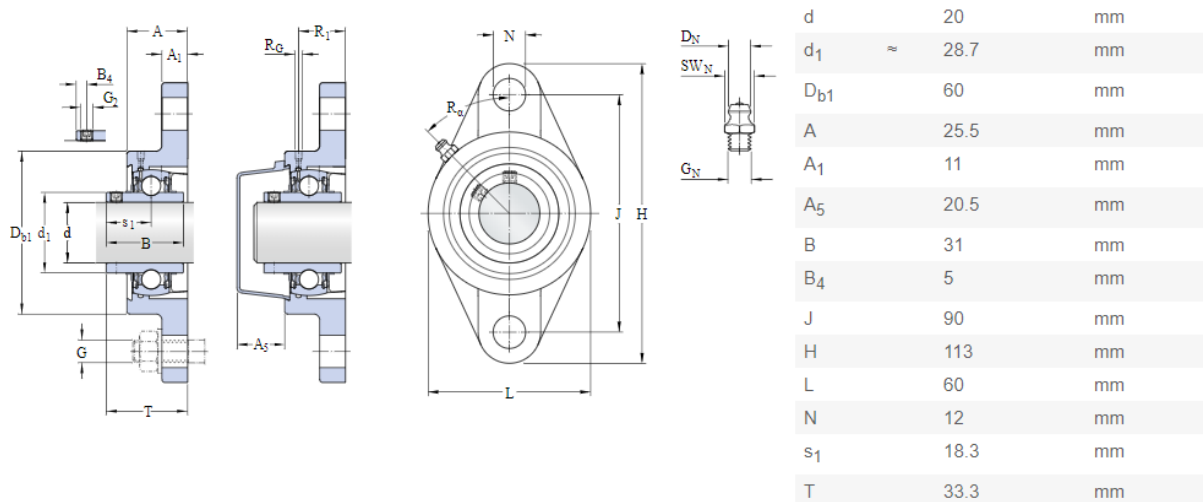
Rodamientos UCFL 204, dimensiones principales. (Fuente: SKF [5])
